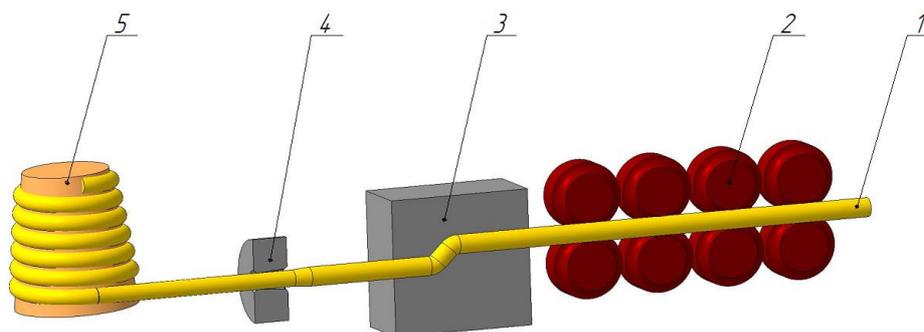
Схема совмещенного процесса «прессование-волочение»: 1 – проволока; 2 – задающее устройство; 3 – равноканальная ступенчатая матрица; 4 – волока в волокодержателе; 5 – барабан наматывающий
